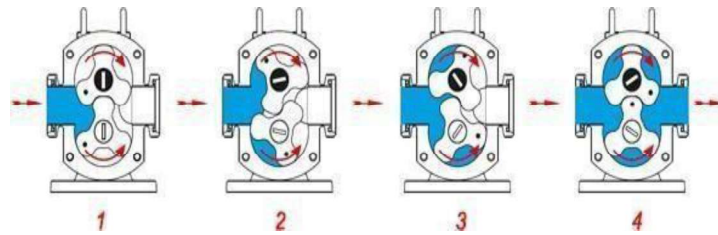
Prinsip Kerja *Lobe Pump
